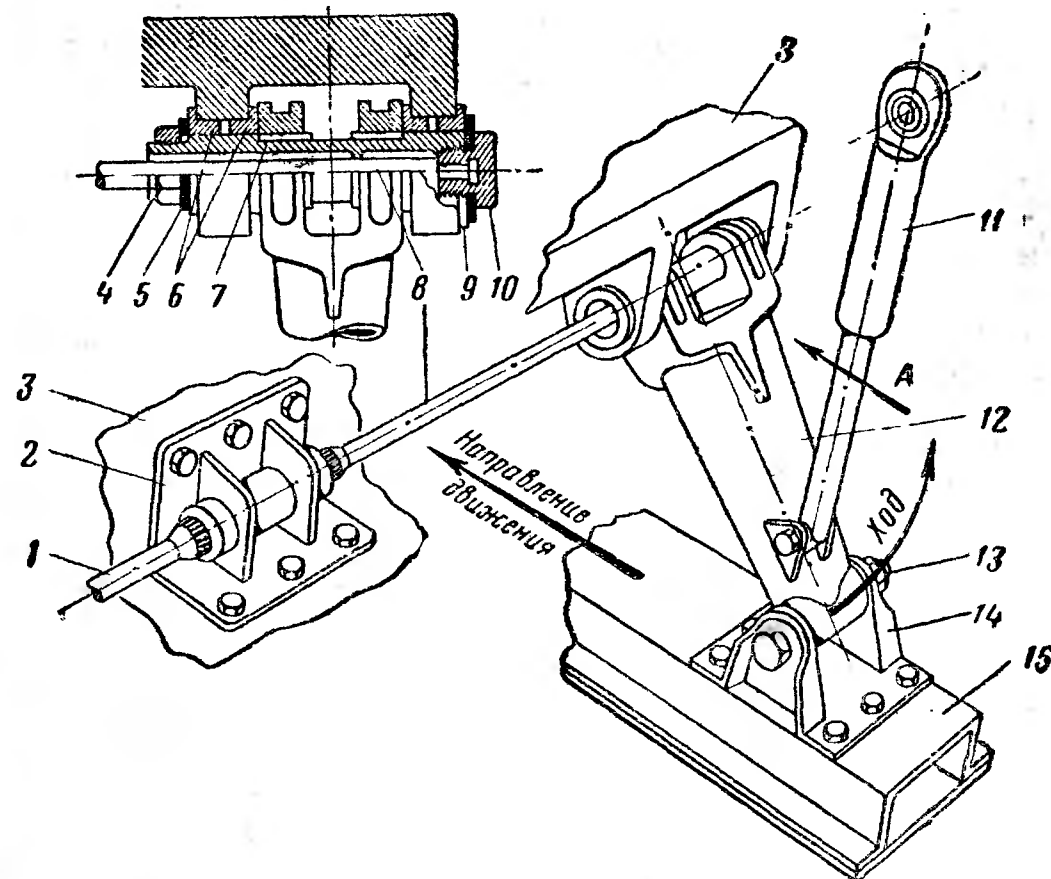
Торсионная подвеска лыж на аэросанях «Ка-36»: 1 — торсионный вал левой задней лыжи; 2 — узел на корпусе крепления торсионных валов; 3 — корпус; 4 — гайка крепления оси; 5 — шайба; 6 — бронзовая втулка в узле корпуса; 7 — ось крепления балки; 8 — торсионный вал правой задней лыжи; 9 — шайба; 10 — центрирующая гайка торсионного вала; 11 — гидравлический демпфер; 12 — балка; 13 — болт с гайкой крепления кабанчика лыжи; 14 — кабанчик лыжи; 15 — лыжа.
